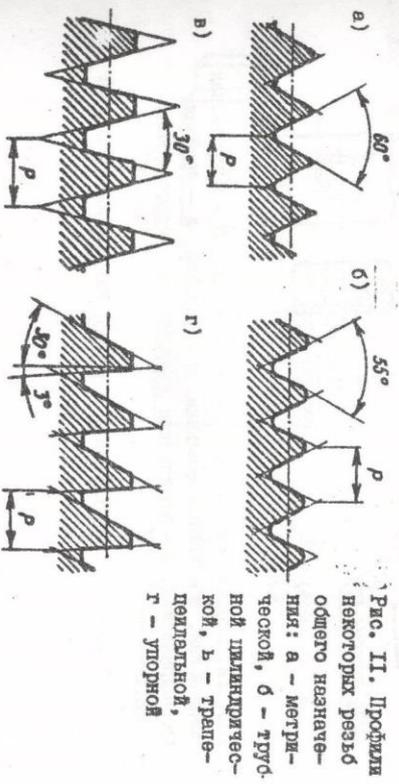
Профили некоторых резьб общего назначения: а - метрической, б - трубной цилиндрической, в - трапециевидной, г - упорной
